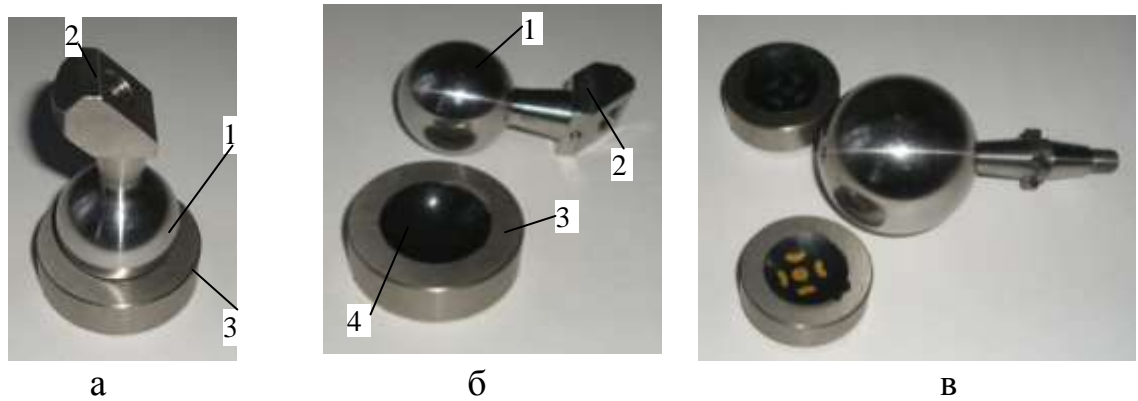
Магнітні шарніри з одностороннім контактом виготовлені з металополімерного композиту: а – шарнір в зібраному стані; б – деталі шарніра; в – формування карманів на поверхні з металополімера
